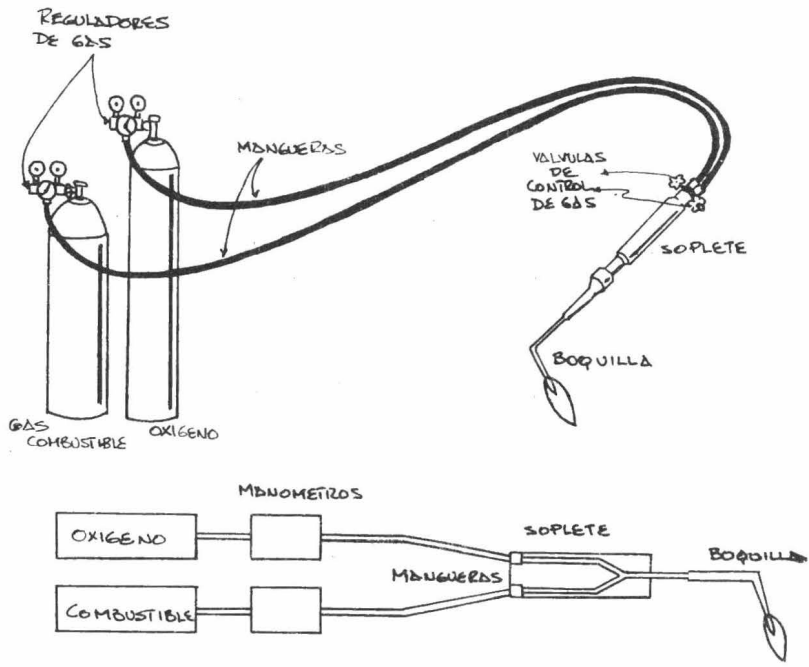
SOLDADURA OXIACETILENICA.
